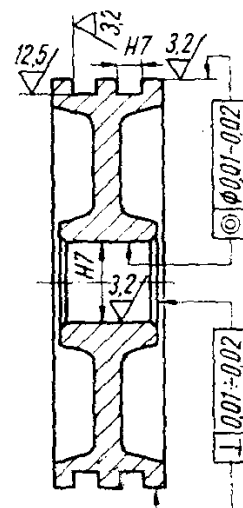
Toleranțe și calități ale suprafețelor la un piston disc.
